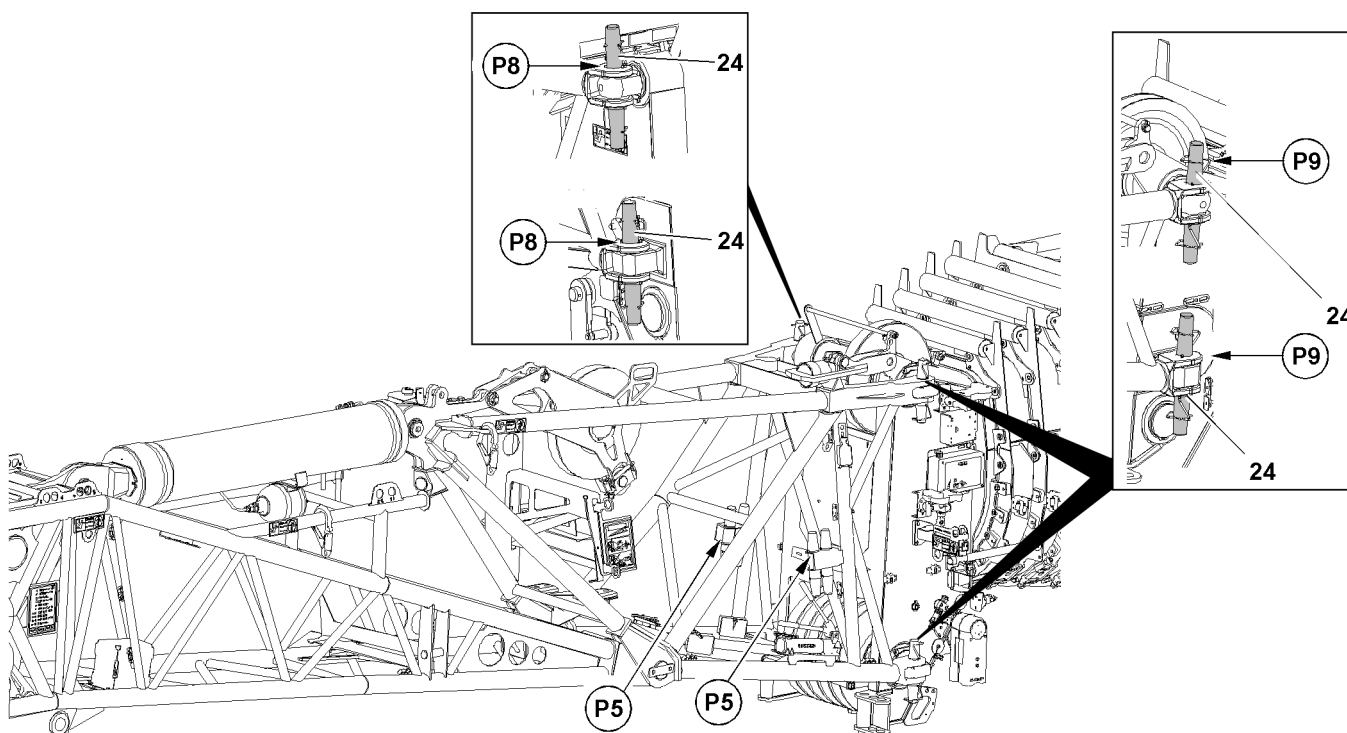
Desmontar o jib rebatível transportado separadamente em posição de operação
